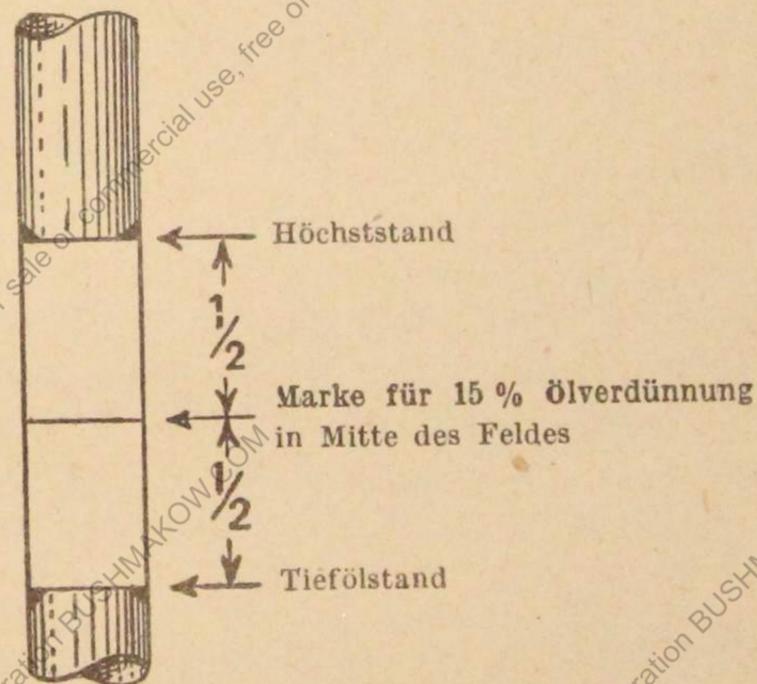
Ölmeßstab für Motoren der Panzer Panther und Tiger
